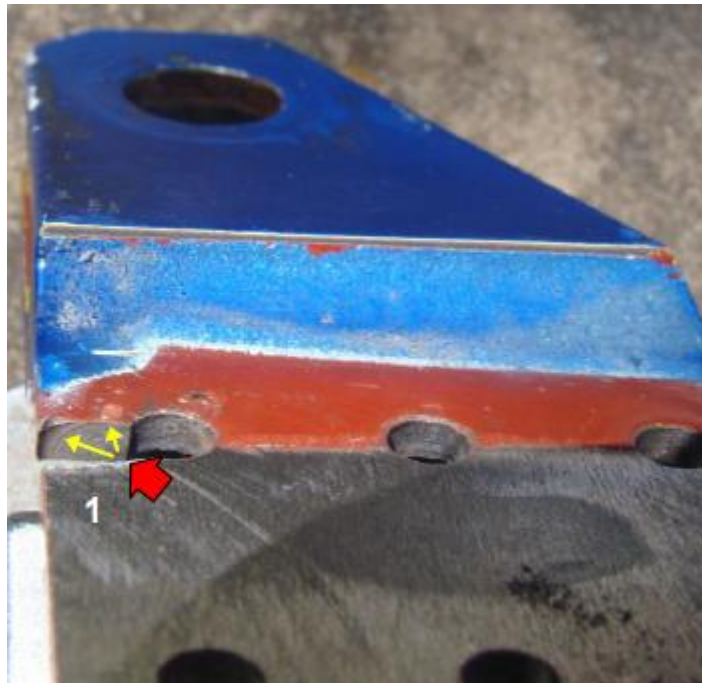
Avance de fisura en el herraje izquierdo. Fuente: investigación JST
